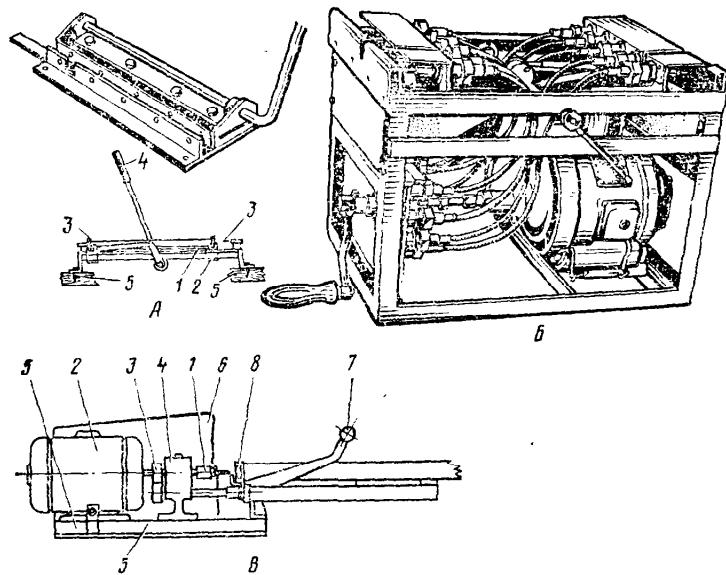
Станки для сверления и прокалывания отверстий в планках рамок:
